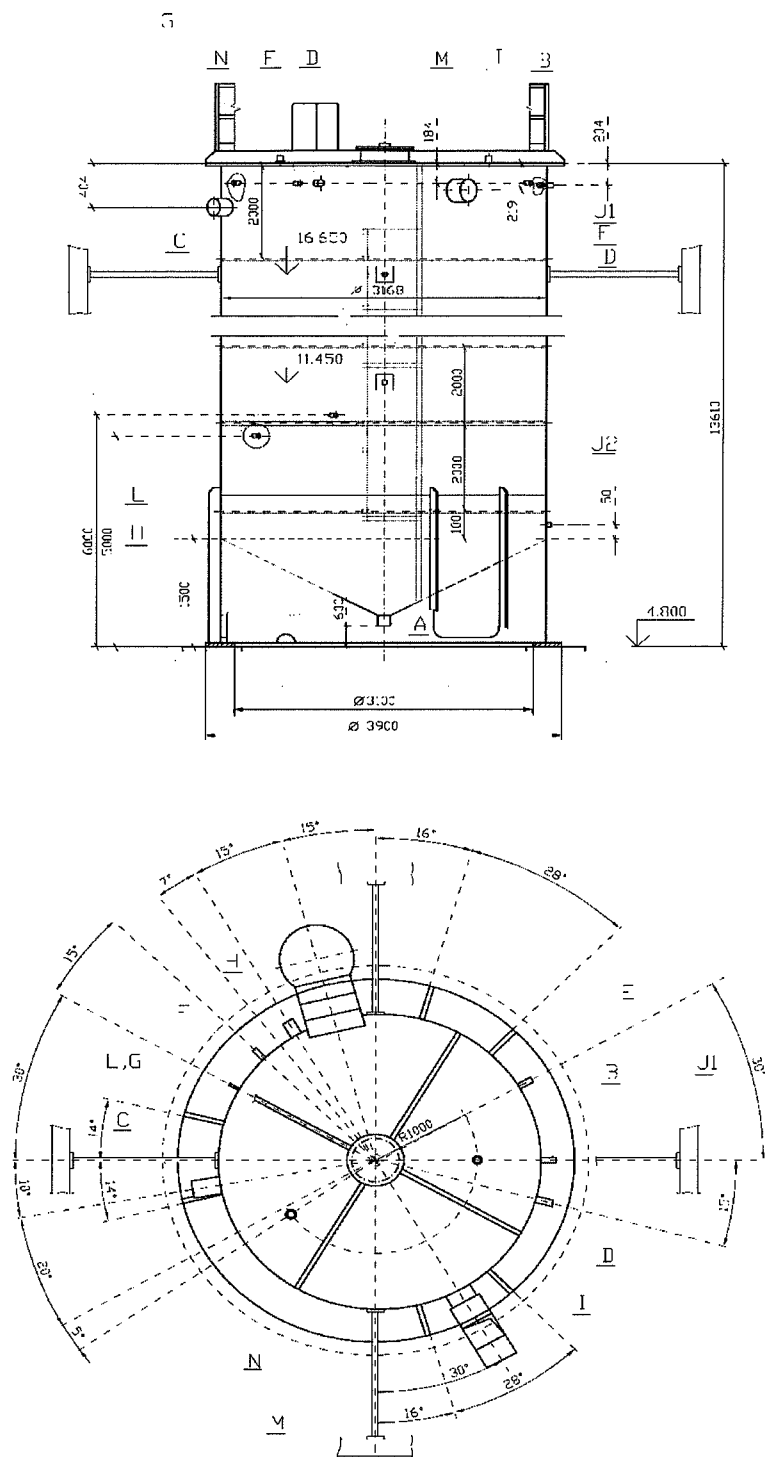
Габаритный чертеж баков трапных вод KPF20BB001, KPF20BB002
